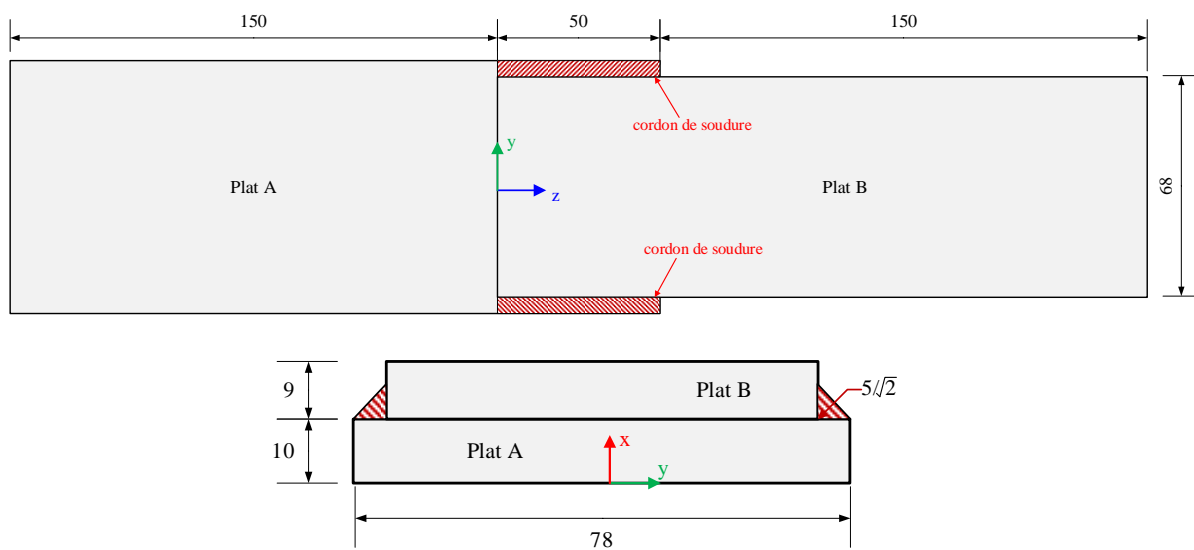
Géométrie de l'éprouvette avec soudure d'angle
